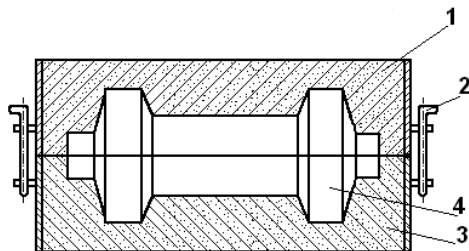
Изготовление верхней полуформы: 1 – верхняя опока; 2 – устройство для центрирования опок; 3 – нижняя опока; 4 – модель
